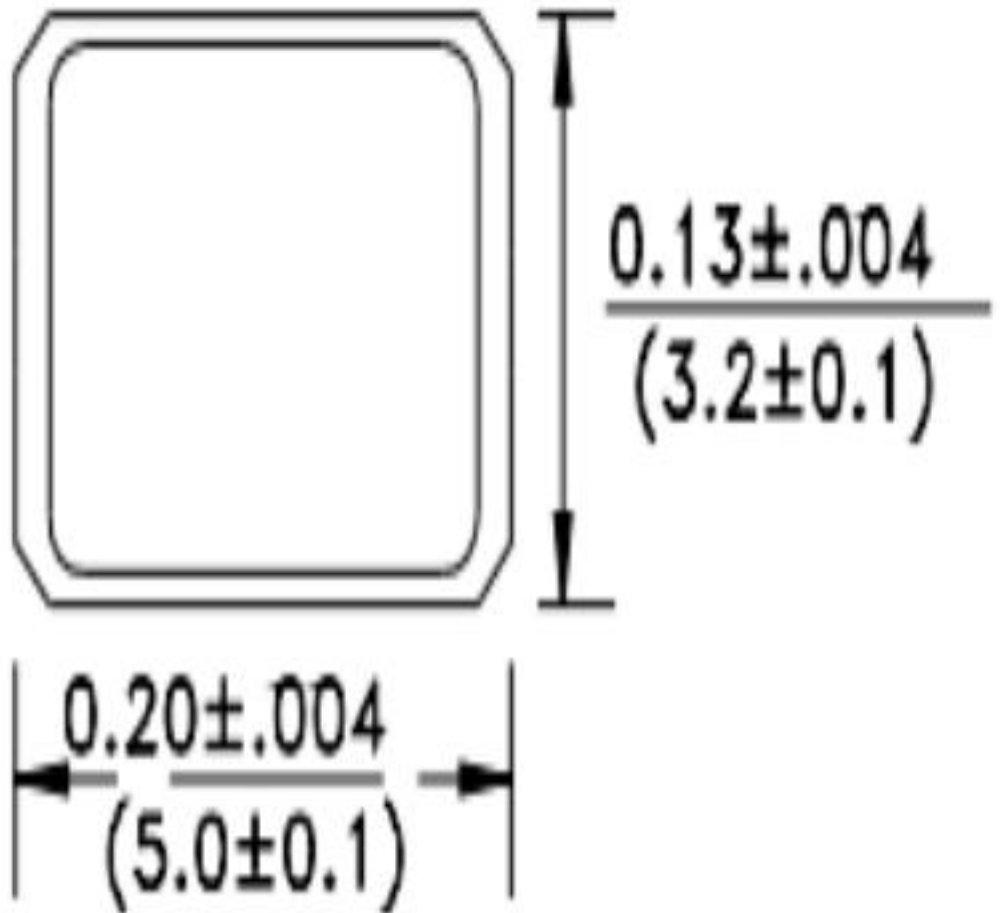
Габаритні розміри кварцового резонатора АВМЗВ-12.000МНЗ-В2
